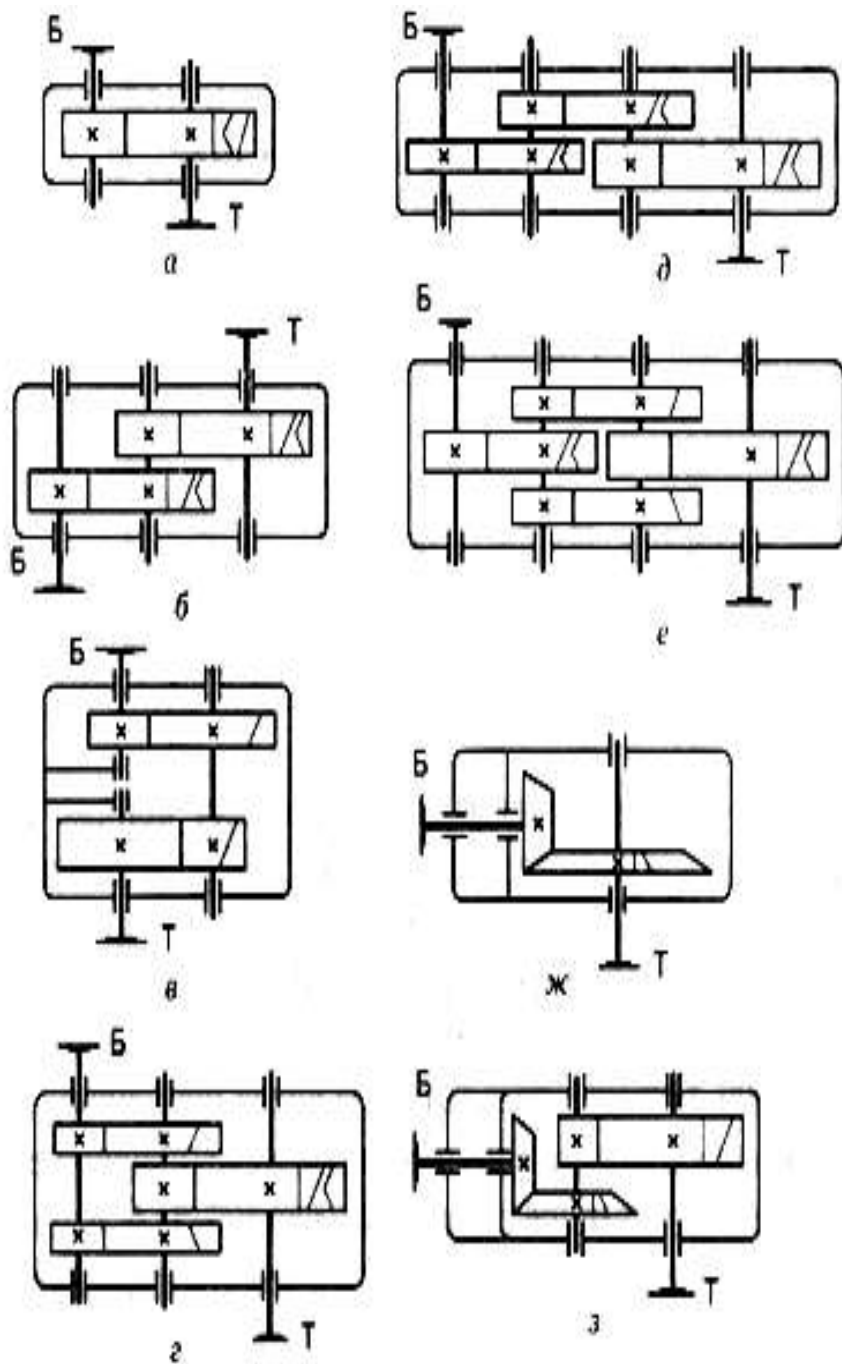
Наиболее распространенные схемы зубчатых редукторов: а — одноступенчатый; б — двухступенчатый развернутый; в — двухступенчатый соосный; г — двухступенчатый с раздвоенной ступенью; д — трехступенчатый развернутый; е — трехступенчатый с раздвоенной промежуточной ступенью; ж — конический; з — коническо-цилиндрический
